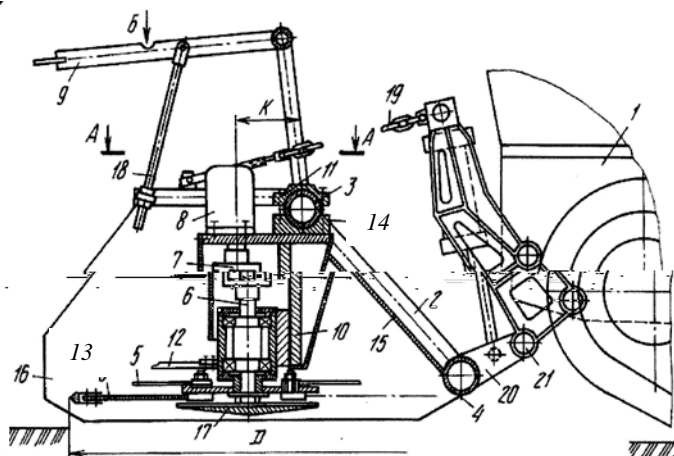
Схема рабочего органа роторного кустореза: 1 – шасси; 2 – рама; 3 – верхняя поперечная балка; 4 – нижняя поперечная балка; 5 – режущие органы; 6 – вал; 7 – муфта; 8 – двигатель; 9 – пригибающе-поддерживающее устройство; 10 – Т-образные кронштейны; 11 и 14 – фиксированные шарниры; 12 – контрнож; 13 – стреловидные наконечники; 15 – отбойная стенка; 16 – боковые стенки; 17 – защитный диск; 18 – жесткие тяги; 19 – гибкие тяги; 20 – кронштейны; 21 – шарниры
